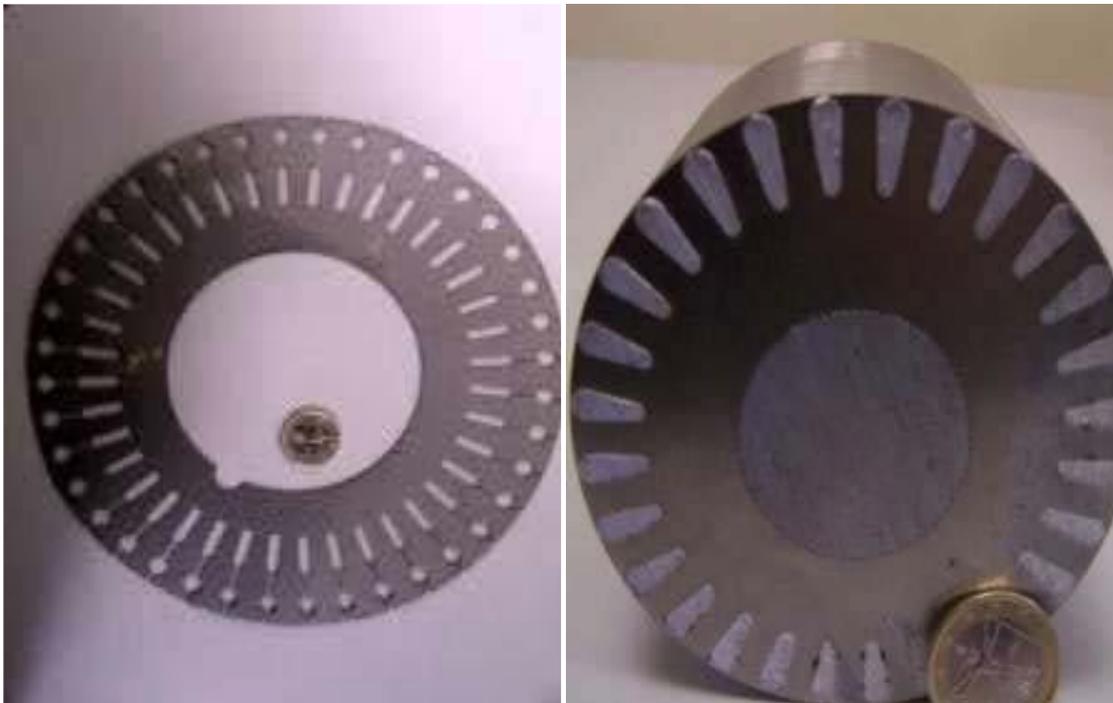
Circuit magnétique constituant le rotor à cage d'écureuil [11]
